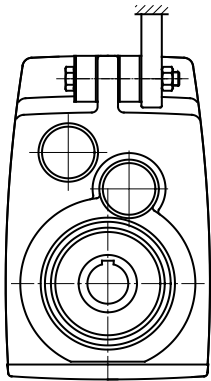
Резиновые амортизаторы (опция G или VG) на редукторах с параллельными валами
